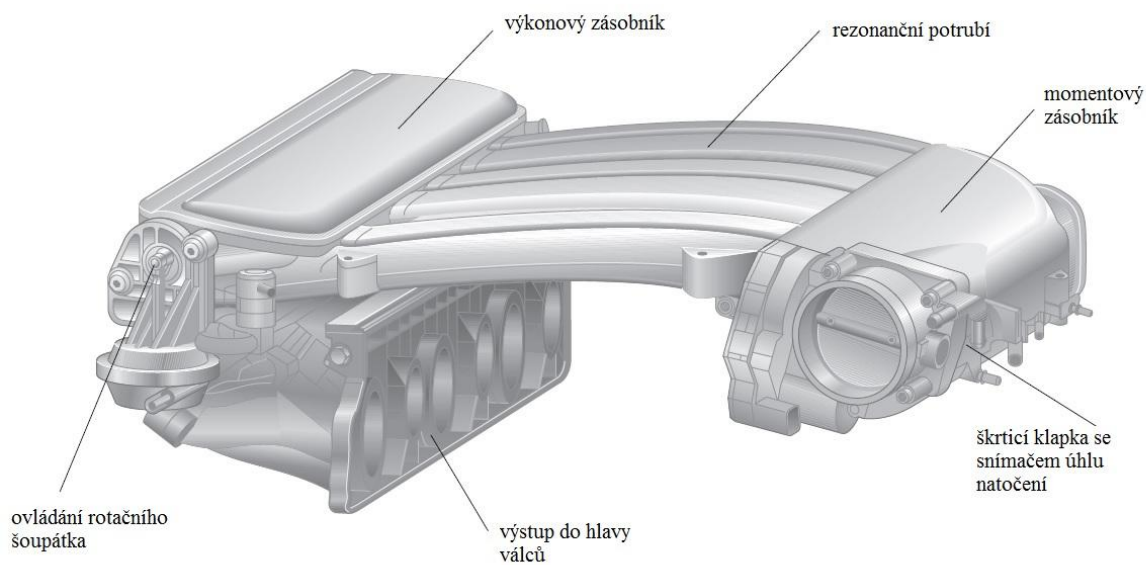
Zobrazení dlouhé a krátké dráhy v případě ovládní rotačním válcem [6]
